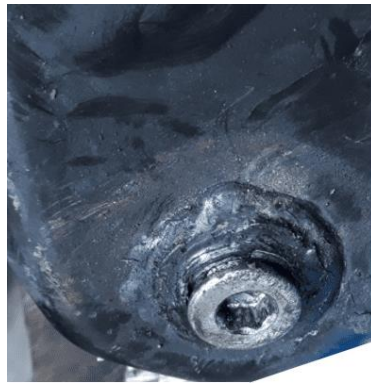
Cárter do óleo com sinais de soldadura.
